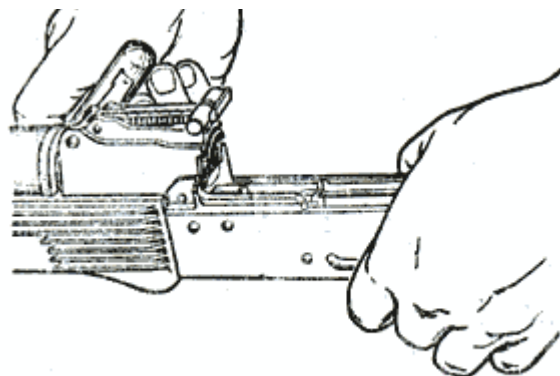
Поворот чеки газовой трубки с помощью пенала принадлежности
